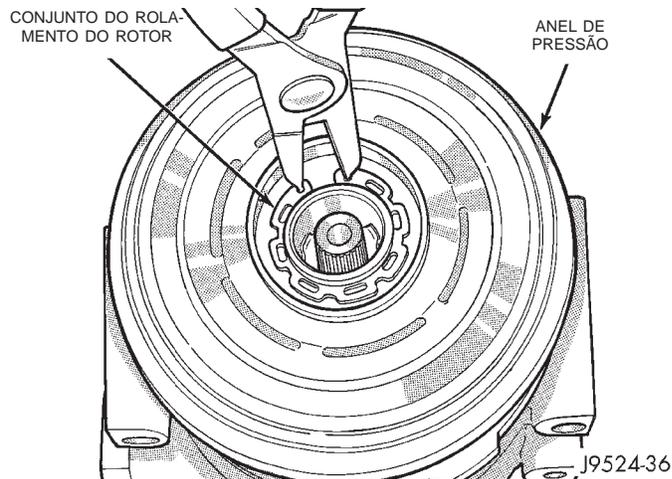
Remoção/Instalação do Anel de Pressão Externo
